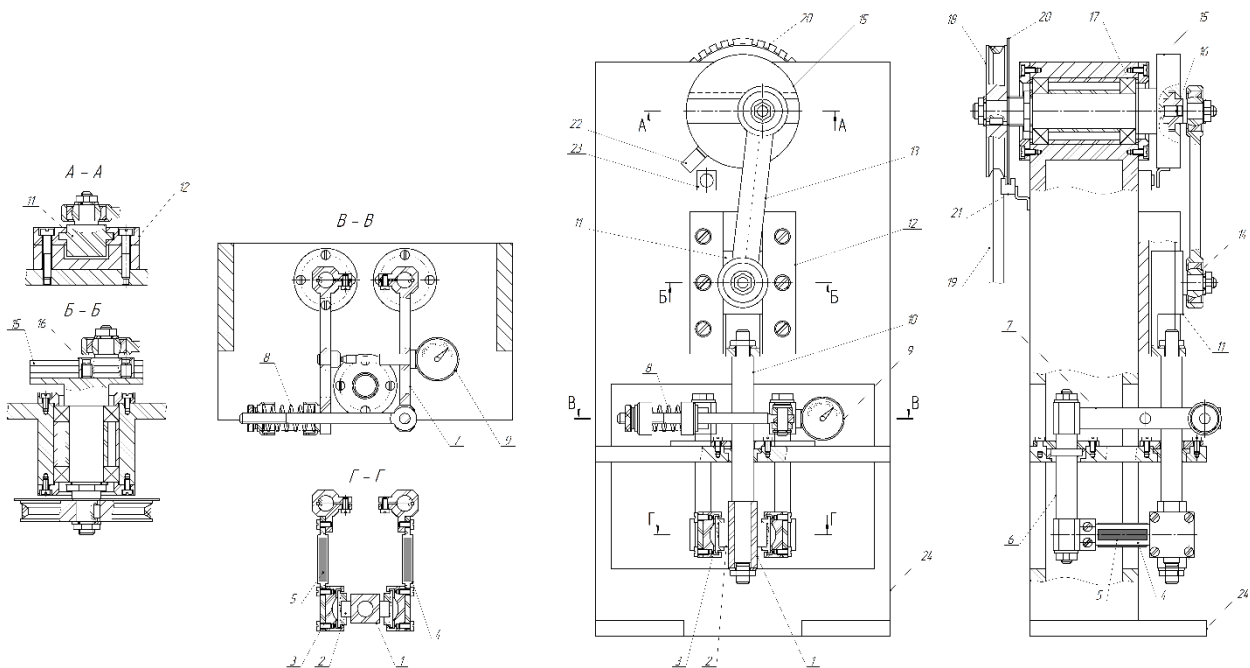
конструкция стенда ВРС-1. Обозначения на рисунке: 1 – подвижный образец; 2 – неподвижный образец; 3 – держатель; 4 – тензобалка; 5 – тензодатчик; 6 – ось держателя; 7 – рычаг; 8 – пружина; 9 – индикатор часового типа; 10 – шток; 11 – ползун; 12 – направляющая; 13 – шатун; 14 – сферический подшипник; 15 – коленвал; 16 – эксцентрик; 17 – шарикоподшипник; 18 – шкив; 19 – клиновидный ремень; 20 – диск с пазами; 21 – датчик частоты вращения; 22 – пластина; 23 – датчик числа циклов; 24 – основание.
